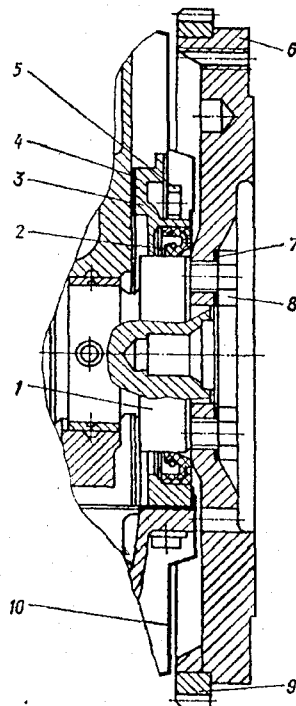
Задний конец коленчатого вала: 1 – вал коленчатый; 2 – манжета коленчатого вала задняя; 3 – держатель манжеты; 4 – прокладка держателя; 5 – болт; 6 – маховик; 7 – шайба болта крепления маховика; 8 – болт крепления маховика; 9 – обод зубчатый маховика; 10 – кожух защитный
